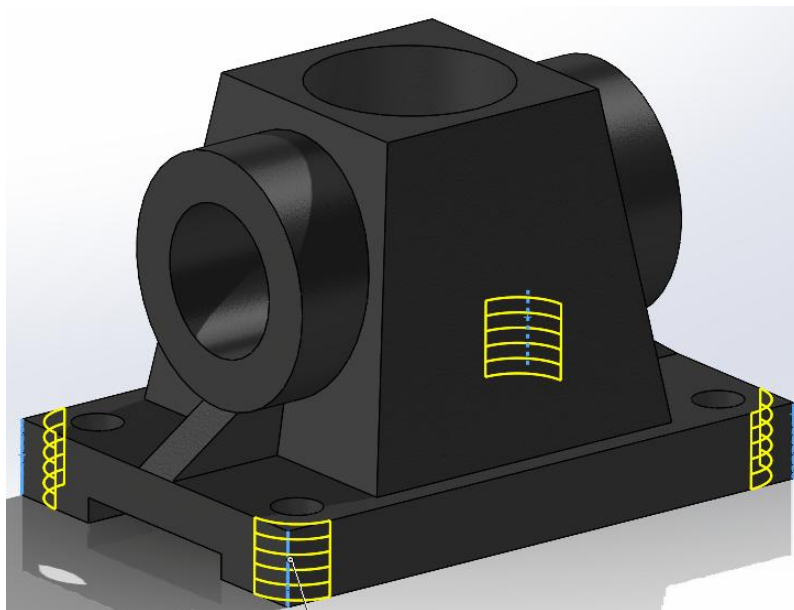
Закруглення кутів за допомогою інструмента Fillet
